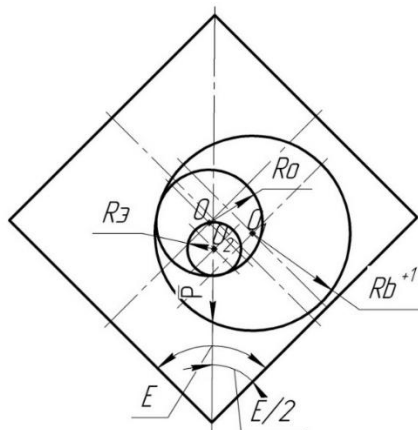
Расчетная схема эксцентрического закрепления
